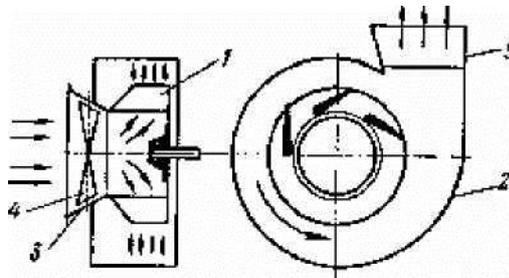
Схема центробежного вентилятора: 1- рабочее колесо; 2 - спиральный кожух; 3 - входной коллектор; 4 - лопатки направляющего аппарата; 5 - диффузор
